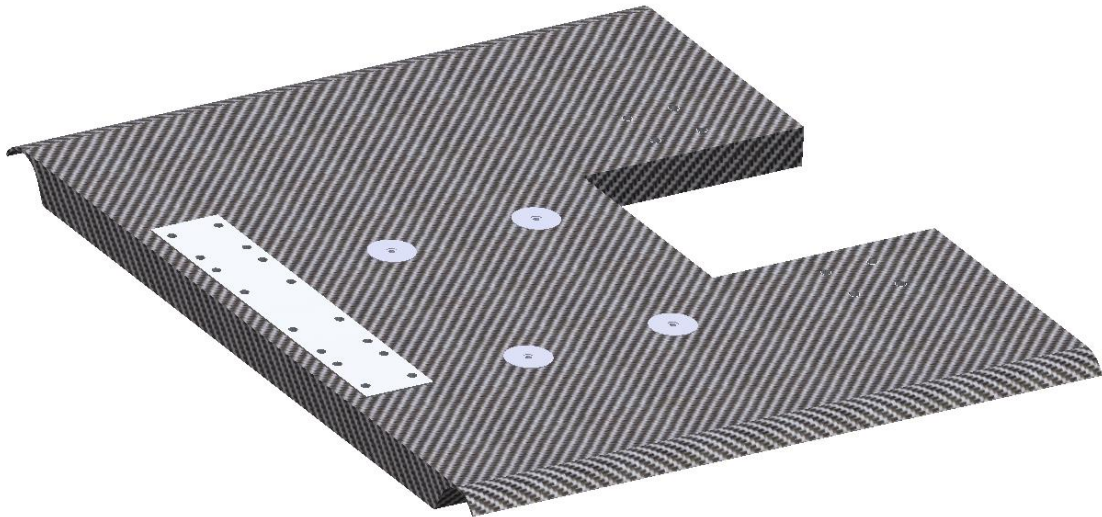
Modelo CAD, vista superior de la plancha central.
